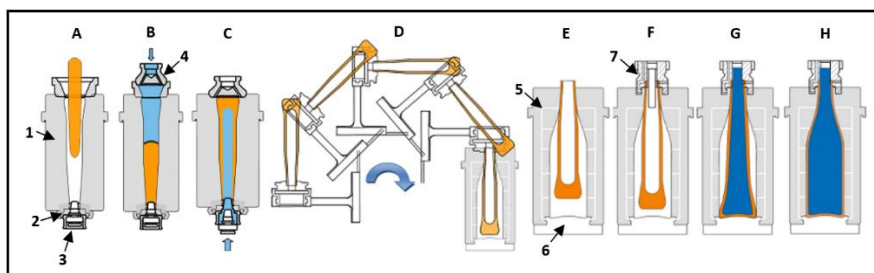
Moldação do vidro de embalagem (adaptado de [18]); 1 – Molde de começar ou contra-molde; 2 – Molde de marisa; 3 – Bico; 4 – Tampão; 5 – Molde de acabar; 6 – Fundo; 7 – Cabeça de sopro.
